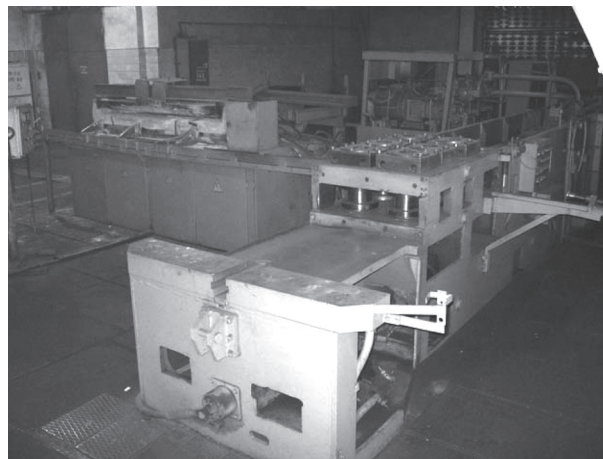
Стан СП-1298М для прокатки заготовок подрессорника
